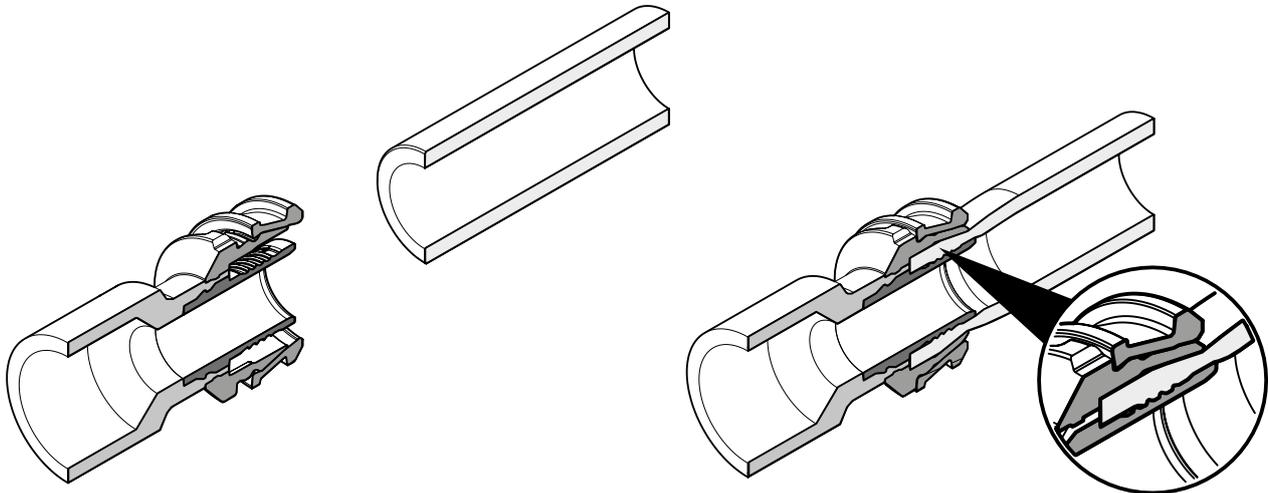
Assemblage Optiflex-Flowpress (ouvert/serti)
